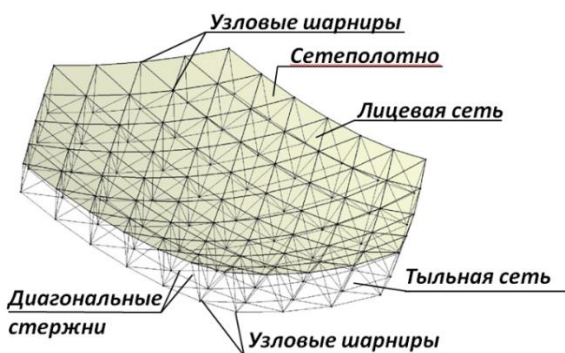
Общий вид рефлектора с ферменным каркасом.
